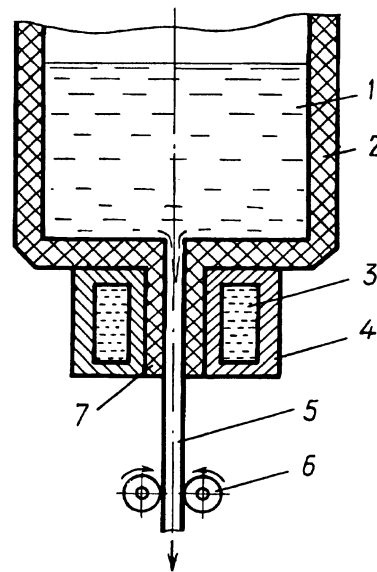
Принципиальная схема установки непрерывного литья: 1 — металл; 2 — тигель; 3 — вода; 4 — корпус кристаллизатора; 5 — отливка; 6 — тянущие валки; 7 — графитовая втулка
